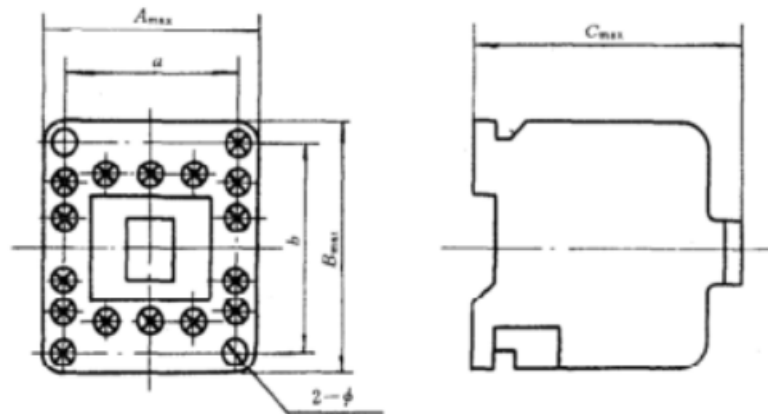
CJX 5-22~40 型交流接触器外形尺寸与安装尺寸
